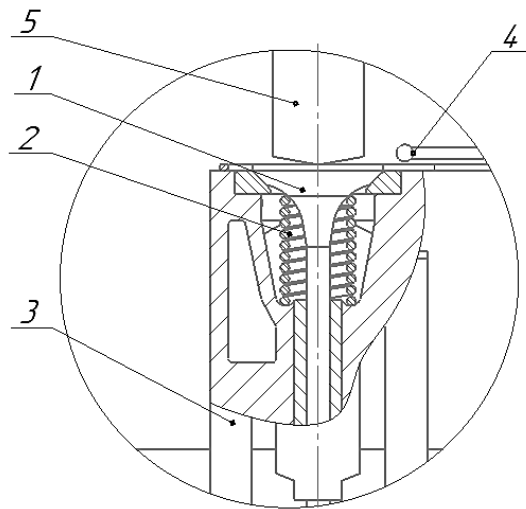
Розташування елементів системи у ГБЦ: 1 – випускний клапан; 2 – зворотна пружина; 3 – головка блока циліндрів; 4 – термопара; 5 – пружинний механізм [3].
